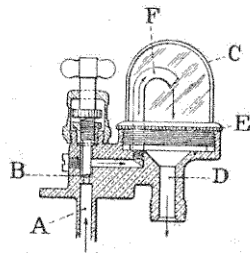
Dispositif de graissage automatique (*Drip-feed lubrication*) des motocyclettes Royal Enfield.
